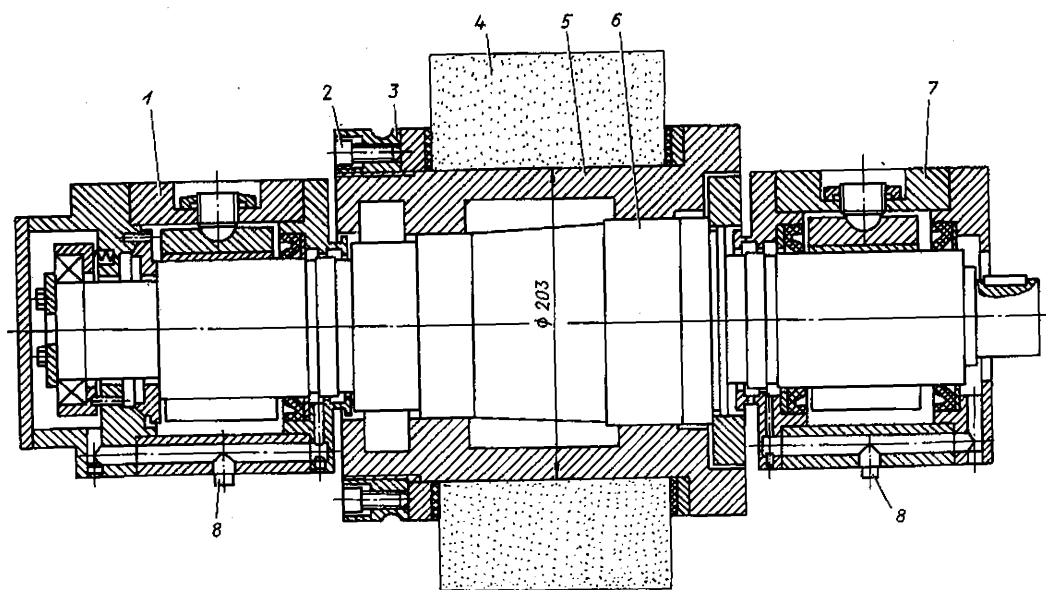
Шпиндель ведущего круга станка ЗМІ84
